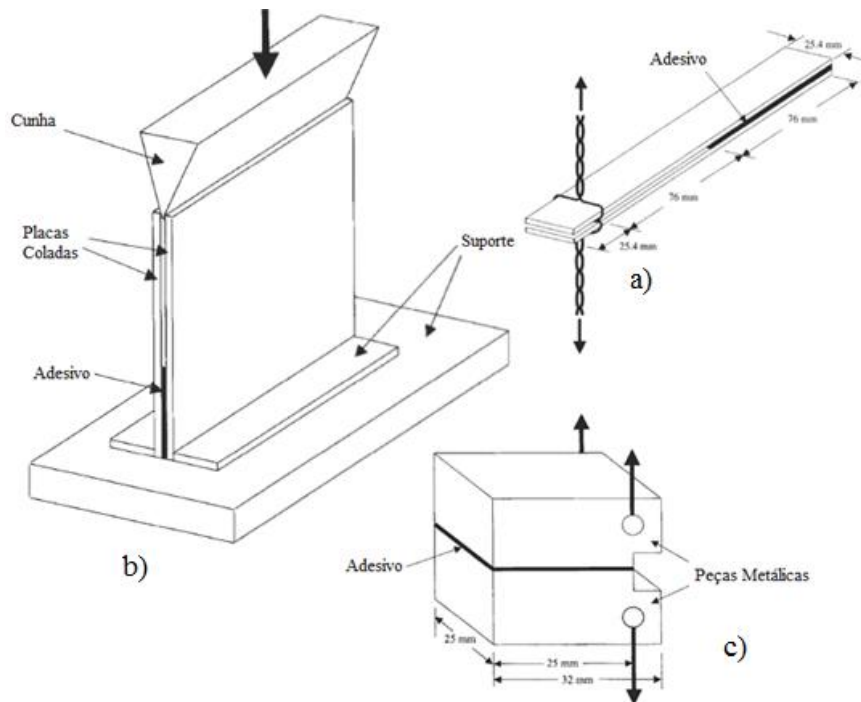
Ensaios de Clivagem ((a) ASTM D3807, (b) ASTM D5041, (c) ASTM D1062) [1]
